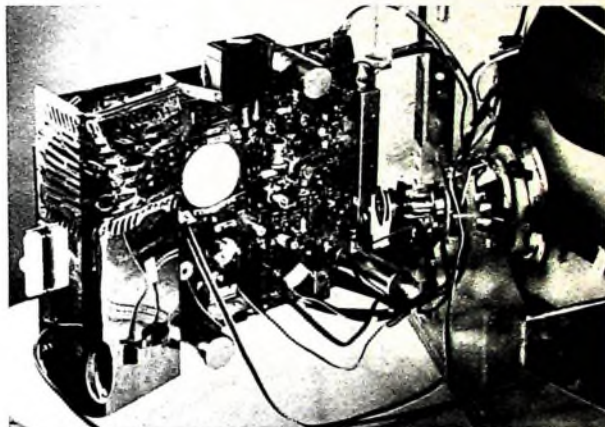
Alle Bauteile des schwenkbaren Chassis sind gut zugänglich
